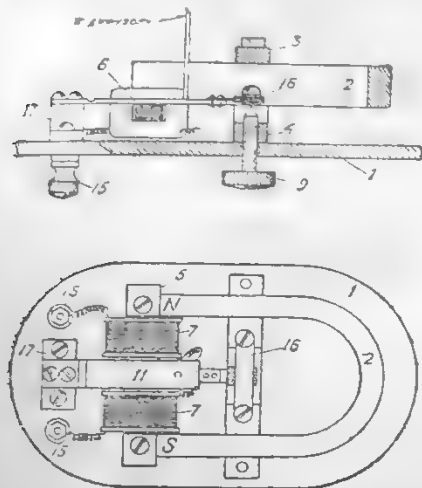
Разрез и план диффузорного громкоговорителя. 1—панель, 2—магнит, 3 и 4—бруски, 5—скобки, 6—сердечник, 7—катушки, 9—регулирующий винт, 11—вибратор, 15—клеммы, 16—плоские пружины, 17—колодки для укрепления вибратора.
